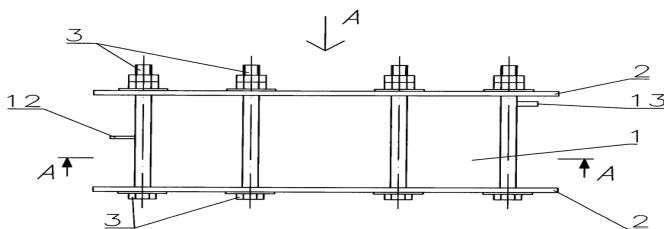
Взрывная камера, сечение А-А [6], где: 1 – металлический наружный корпус в форме цилиндра; 2 и 3 – верхние и нижние упорные кольца; 12 – вакуумная трубка; 13 – штуцер.
